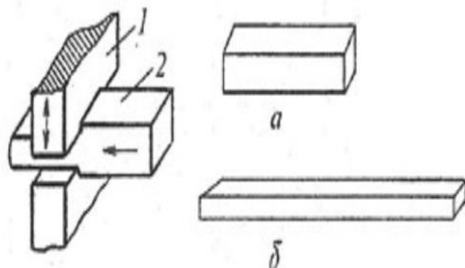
Схема протяжки заготовки 2 узкими бойками 1:
